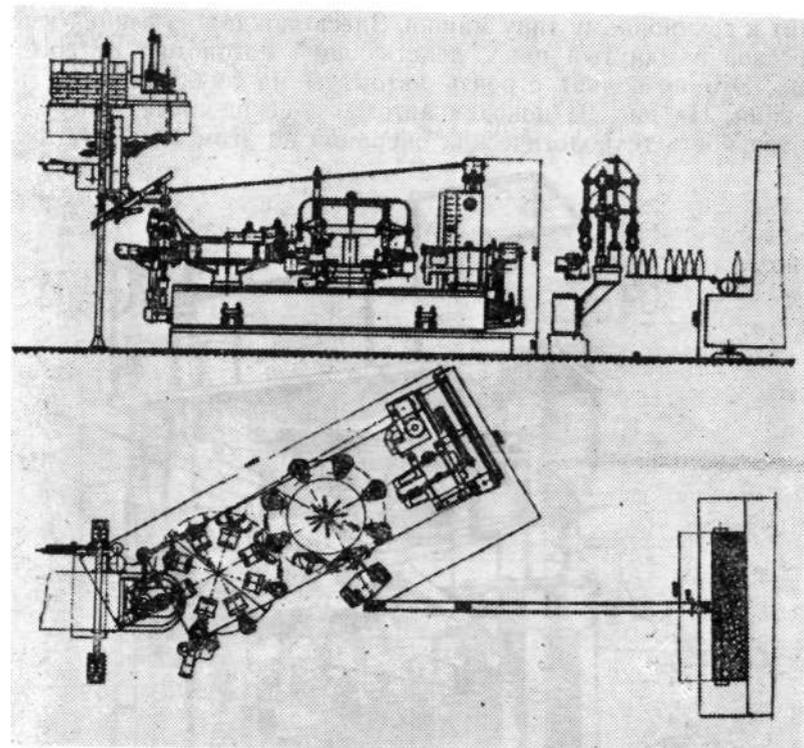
Общий вид установки АБ-6 для производства бутылок.
